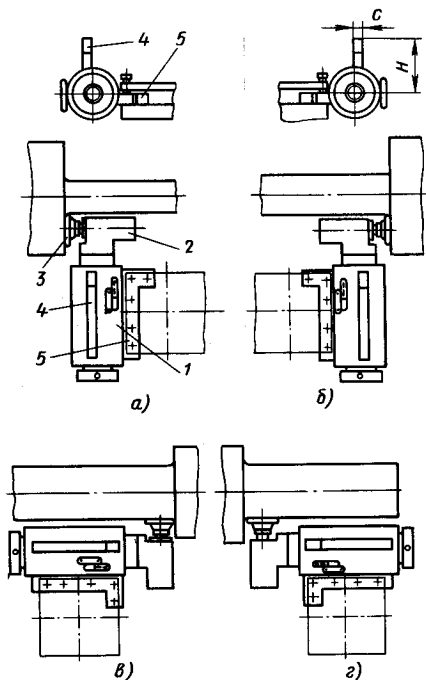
Схемы установки однороликовых приспособлений для обкатывания поверхностей на токарном станке
